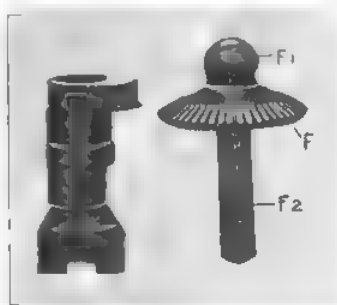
Achse mit Kegelrad u. Kugelgelenk; links: Pumpenexcenter und Cardangelenk.
